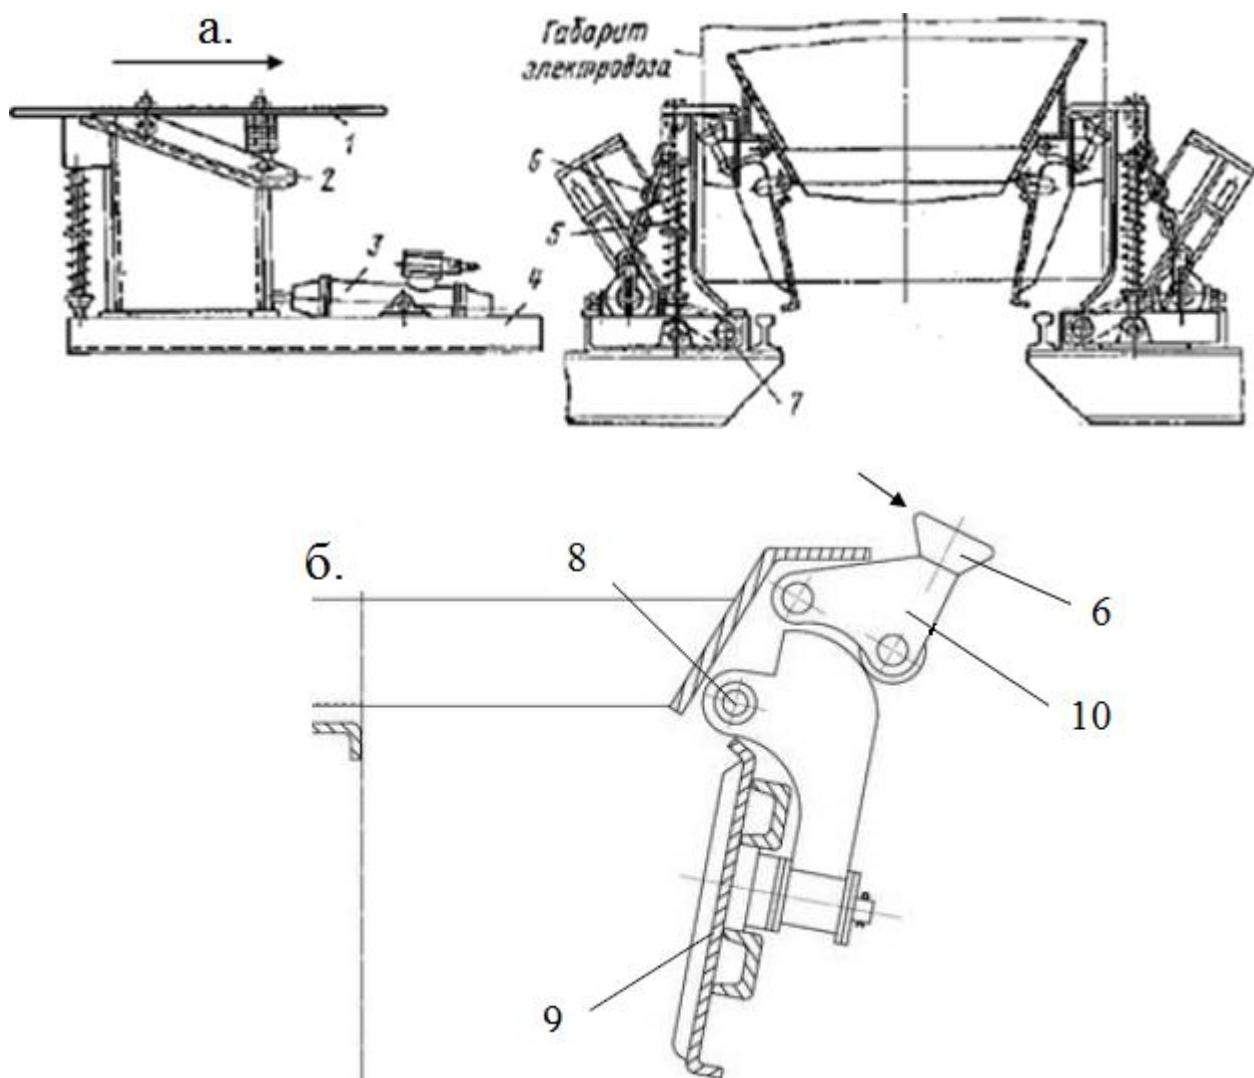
Устройство для закрывания днищ (клапанов): а – общий вид, б – положение роликового замкового устройства при открытом днище
